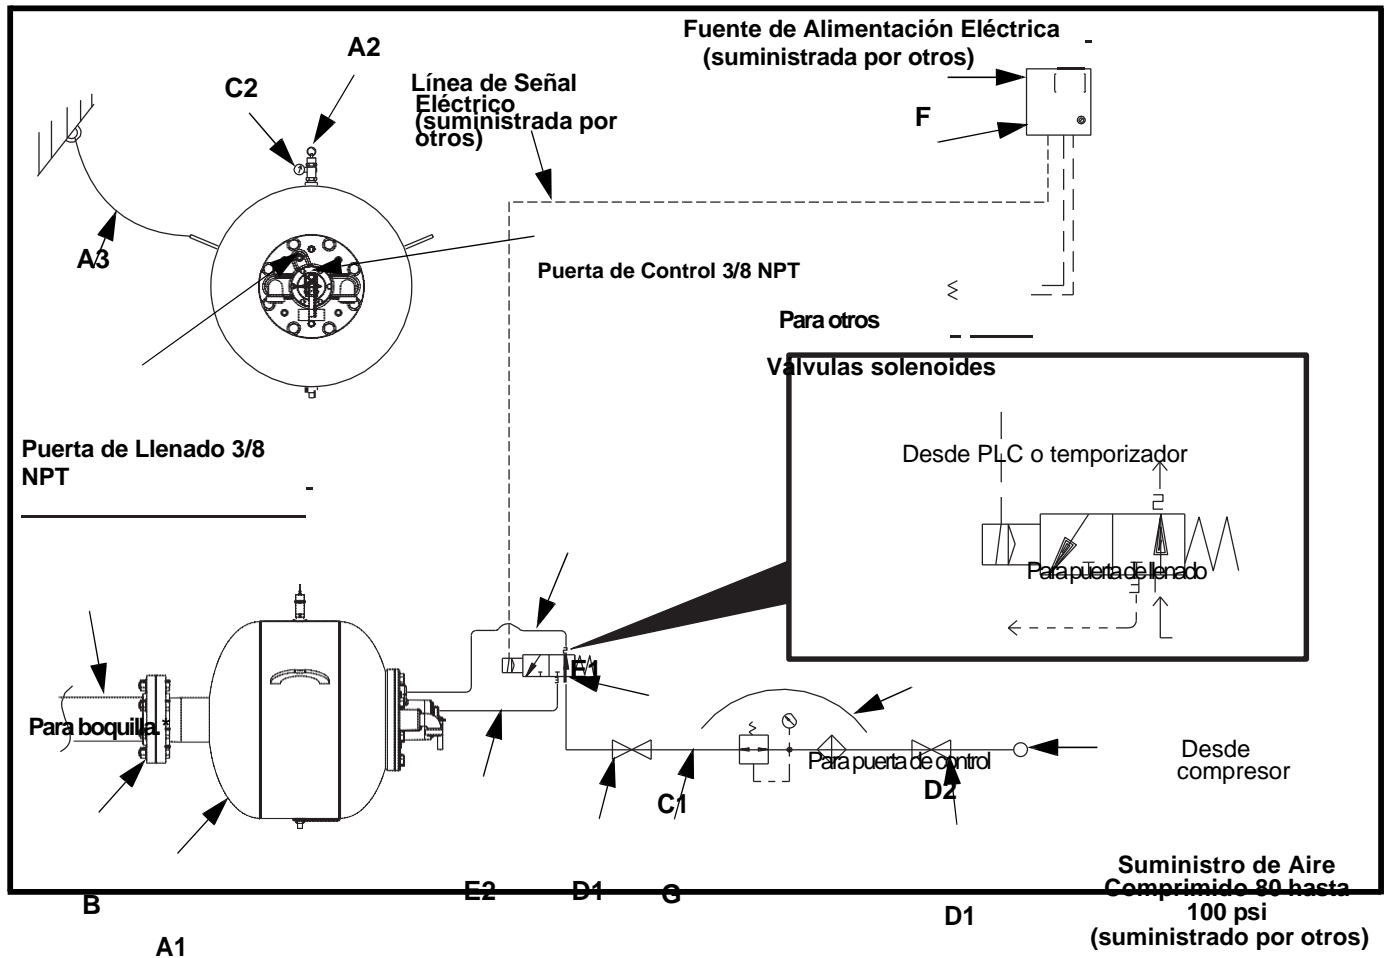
Detalle de la Tubería para Válvula Solenoide Normalmente Abierta
